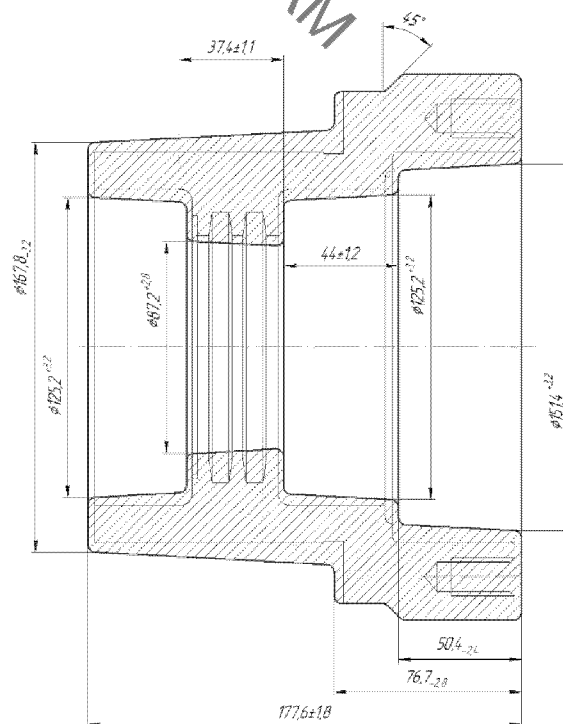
Ескіз заготовки в оболонковій формі
